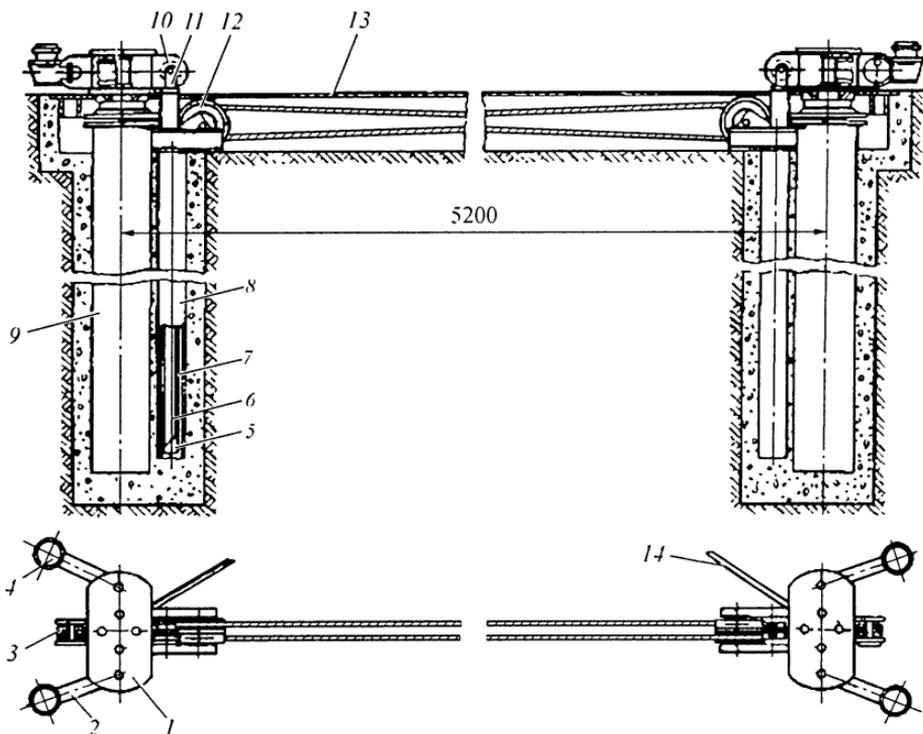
Двухплунжерный электрогидравлический подъемник П-111: 1 — плата платформы; 2 — балка платформы; 3 — барабан; 4 — подхват; 5 — четырехклиновый зажим троса; 6 — голкающая труба синхронизирующей стрелы; 7 — трос; 8 — кожух толкающей трубы; 9 — цилиндр в сборе; 10 и 12 — малый и большой блоки соответственно; 11 — предохранительный стержень; 13 — настил, 14 — маслопровод
